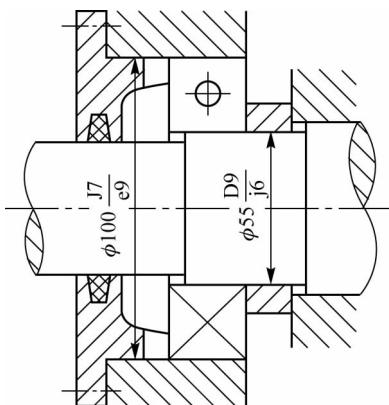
轴承盖与孔、轴承挡圈与轴的配合
